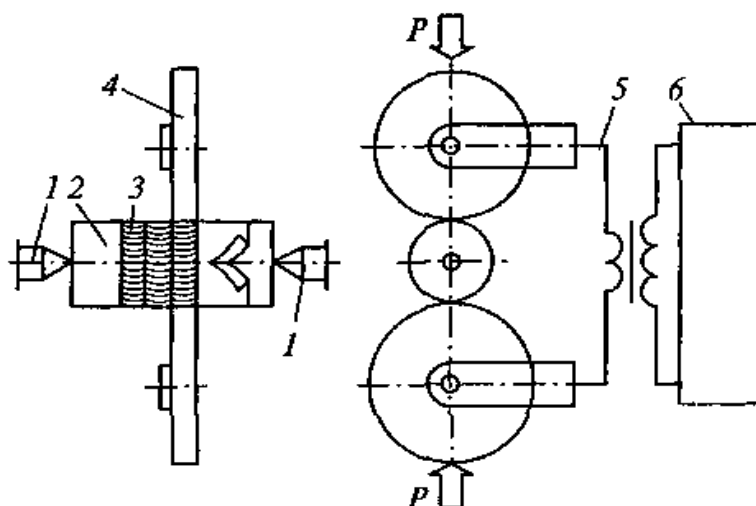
Схема электроконтактной приварки ленты на установке 011-1-02Н: 1- центр; 2-восстанавливаемая деталь; 3-лента; 4-ролик; 5-трансформатор; 6 – прерыватель тока; P- прижимное устройство.
